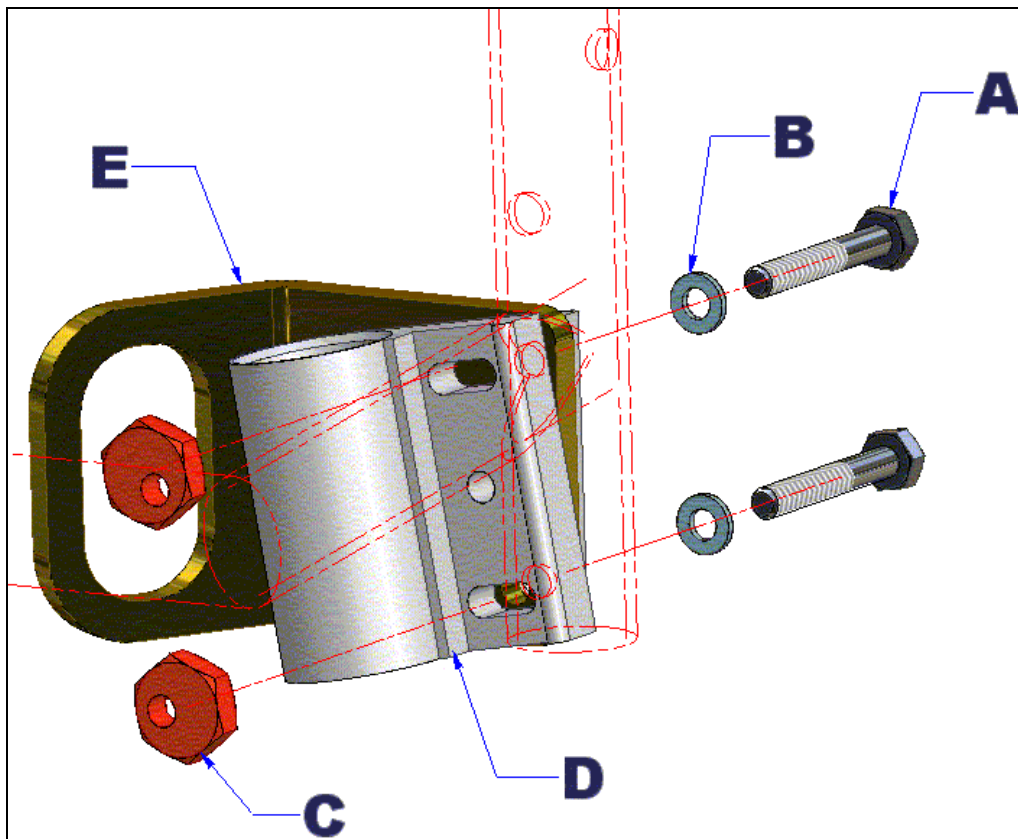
A : Installation des anneaux d'ancrage AVANT.
